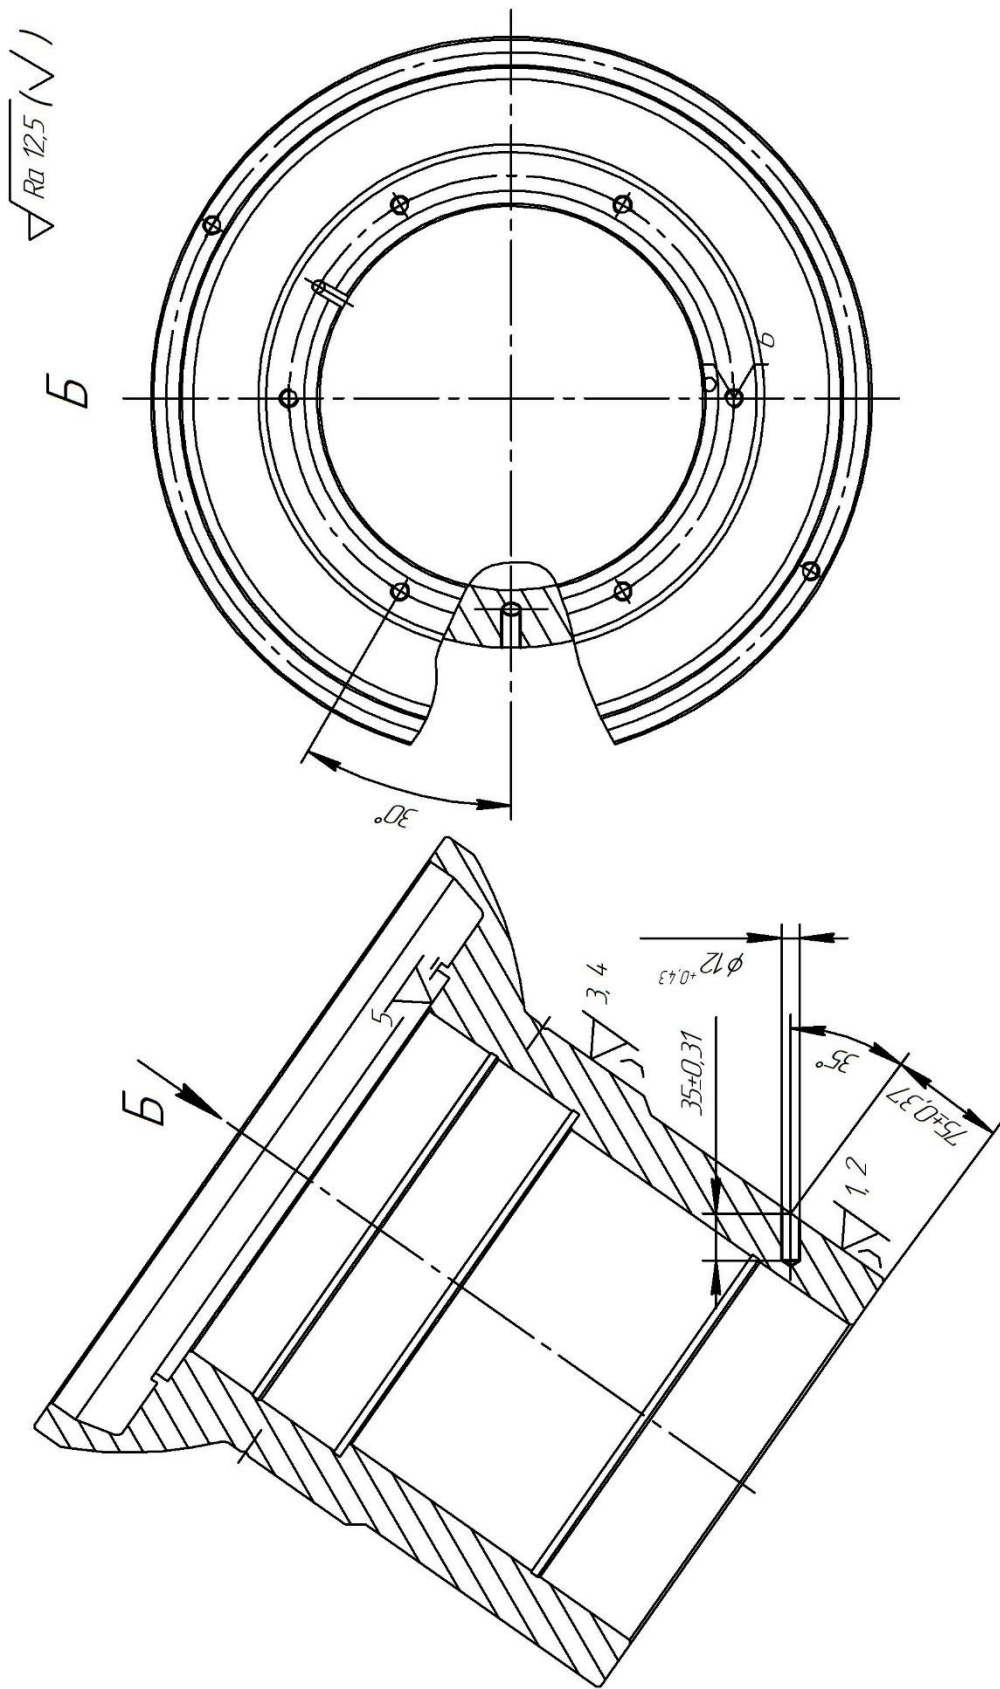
Схема базування заготовки на операції 060 горизонтально-розточувальній (установ Б)
